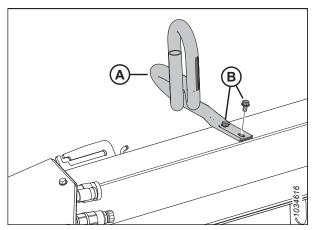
Nouveau guide de flexible installé sur la plateforme – Toutes les plateformes D1 hormis les couteaux doubles D115 et D120
